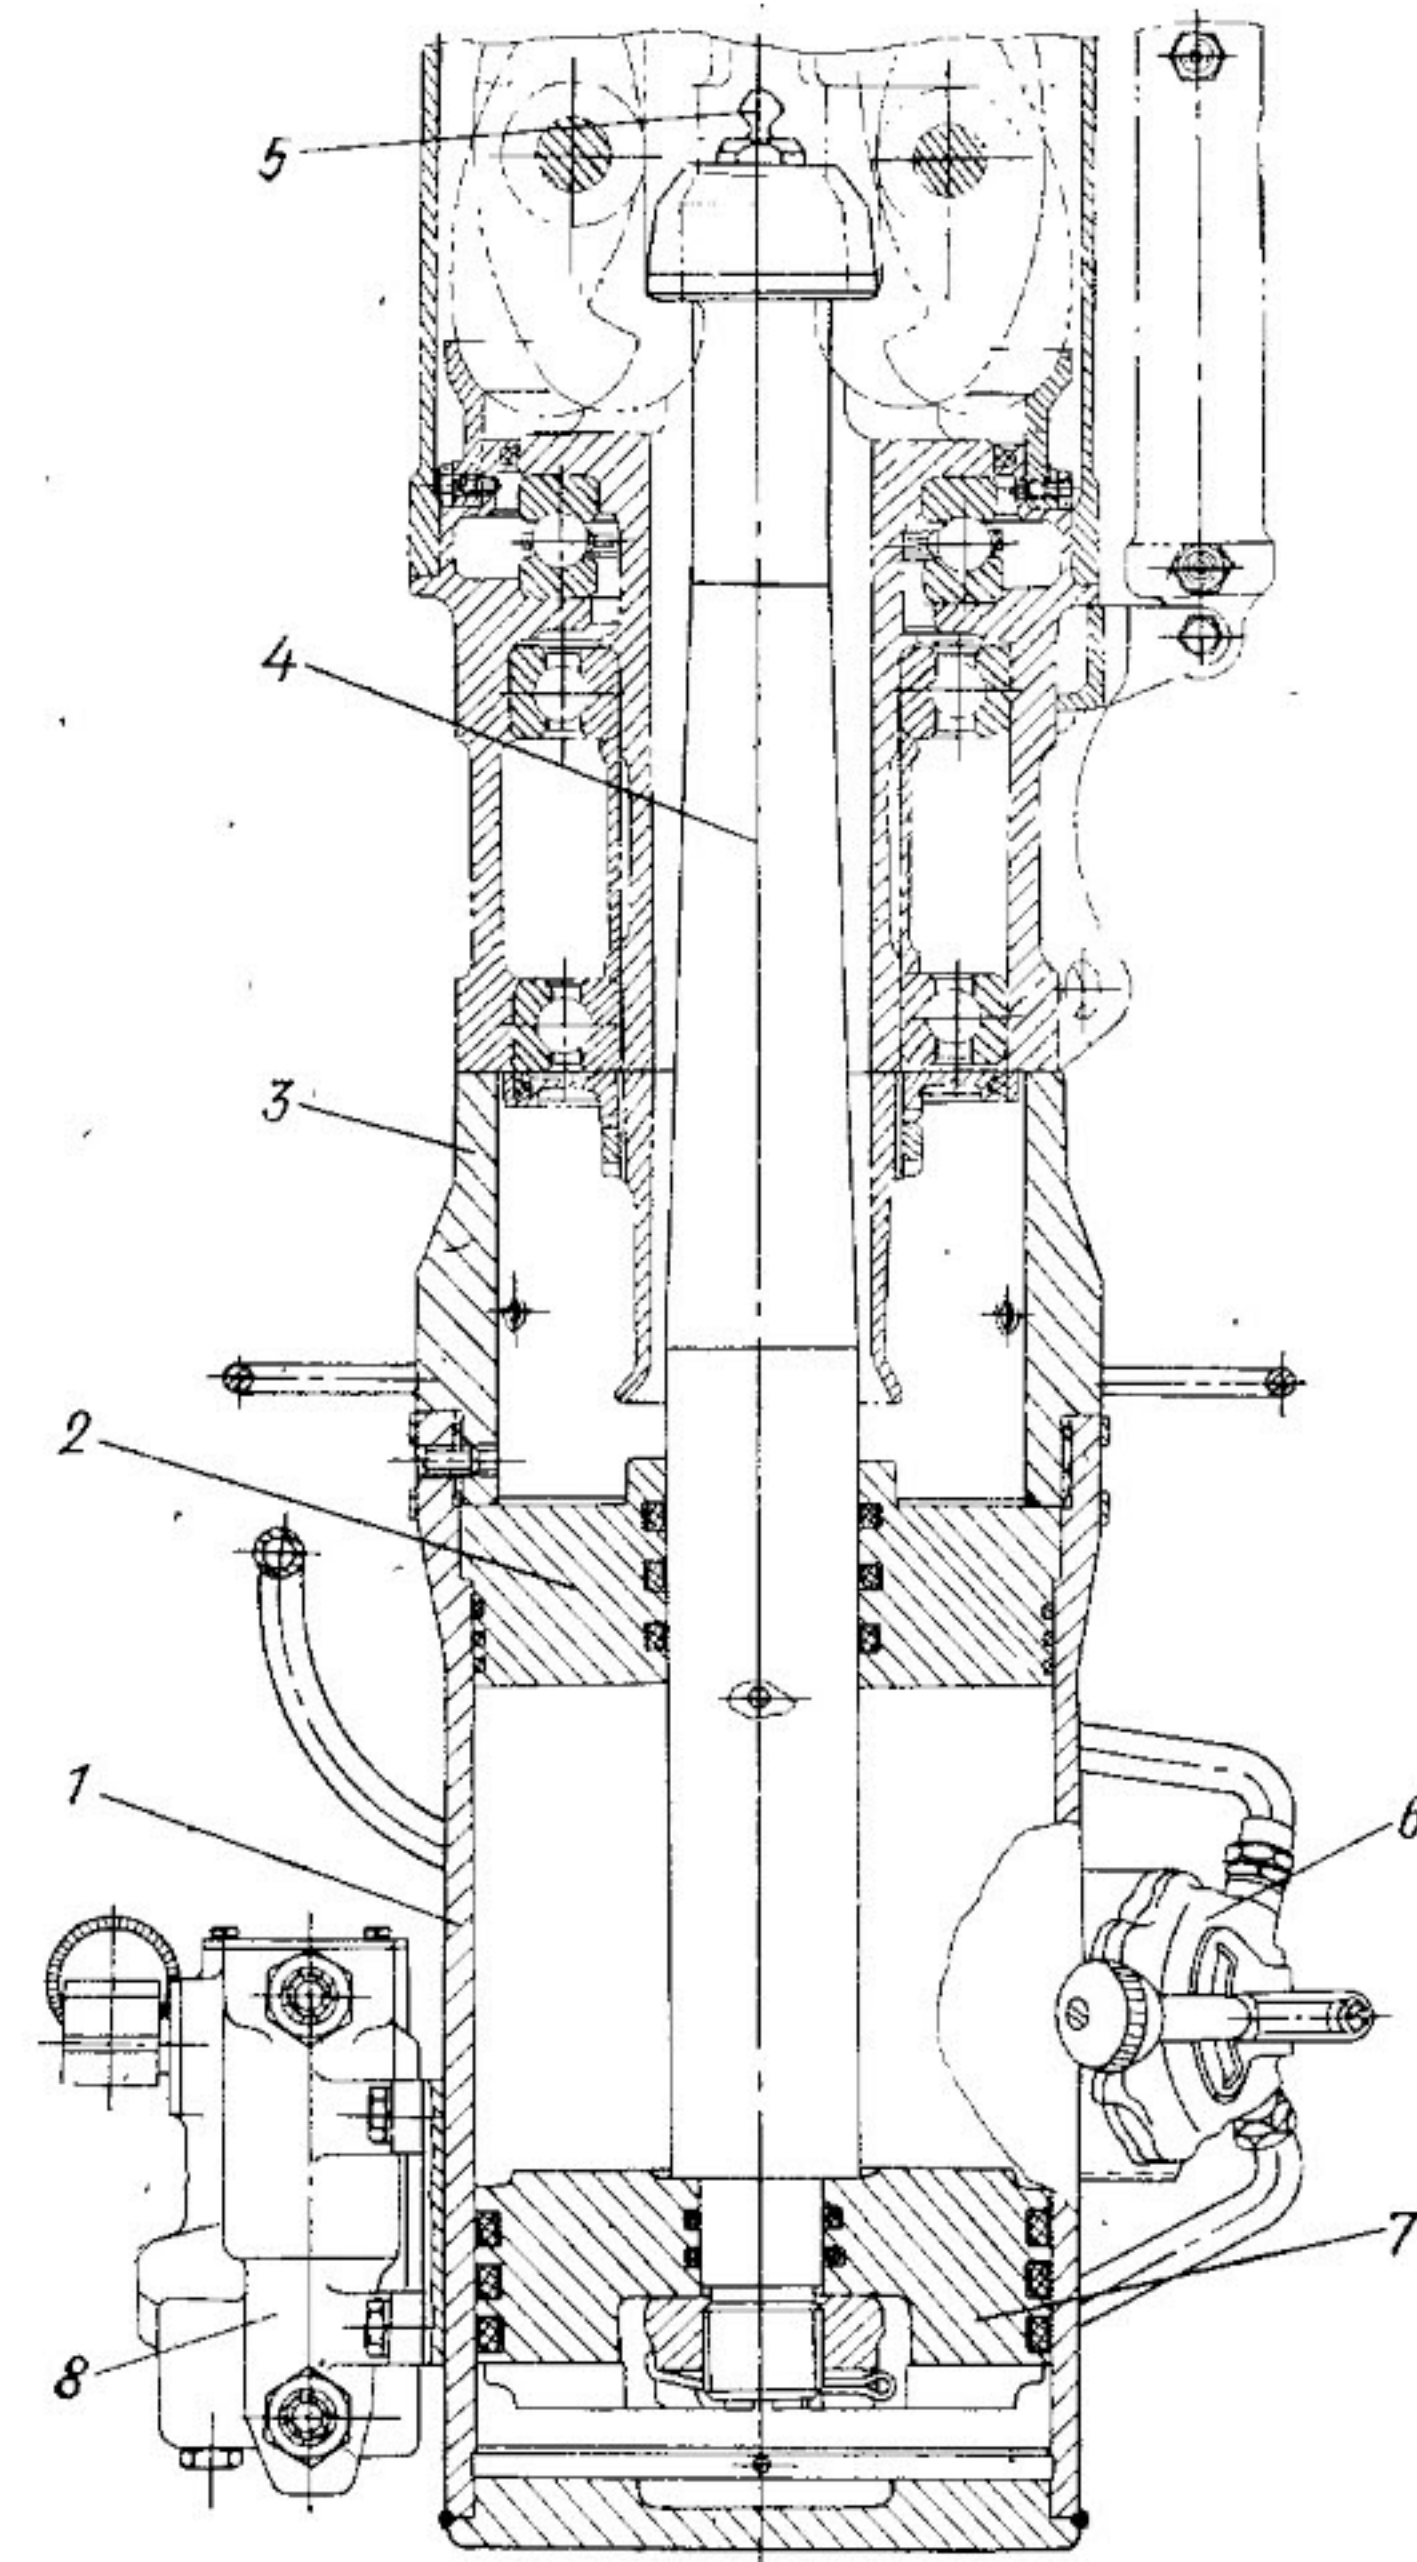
Гидроцилиндр приспособления для испытания наружной подвески:
